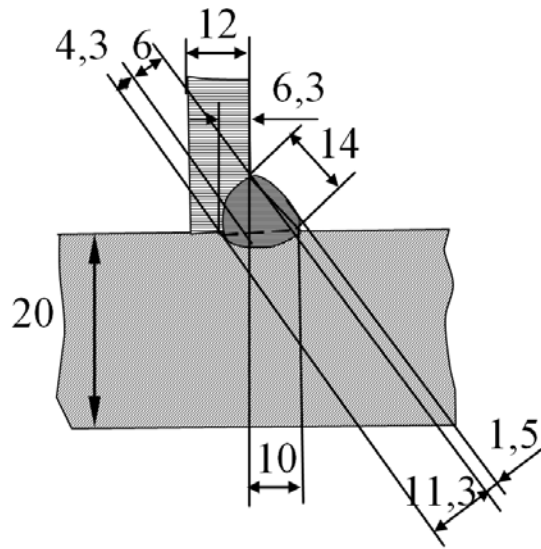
Геометрические размеры сварного шва, мм
